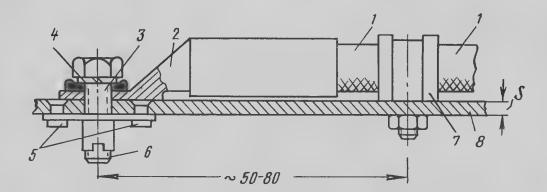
Присоединение минусового провода к корпусу объекта с помощью болта и самоконтрящейся гайки (3-й способ):
